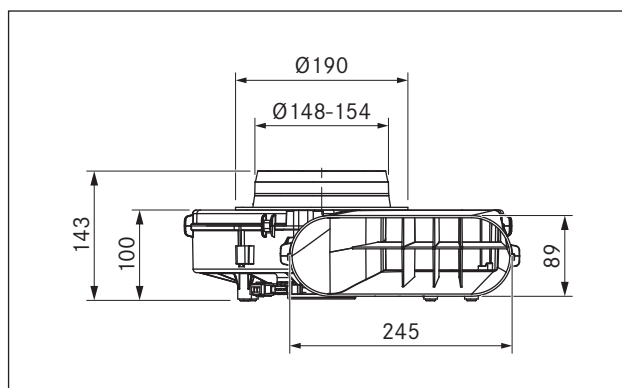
PKAS, PKASAB dimensiones del aparato vista frontal
